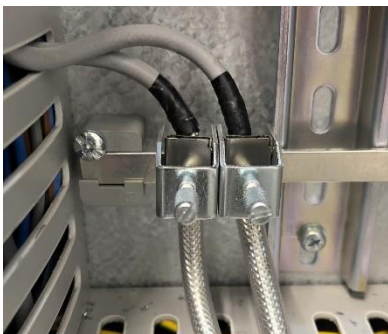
Kabelanschlussklemmen für Schaltschrankmontage
